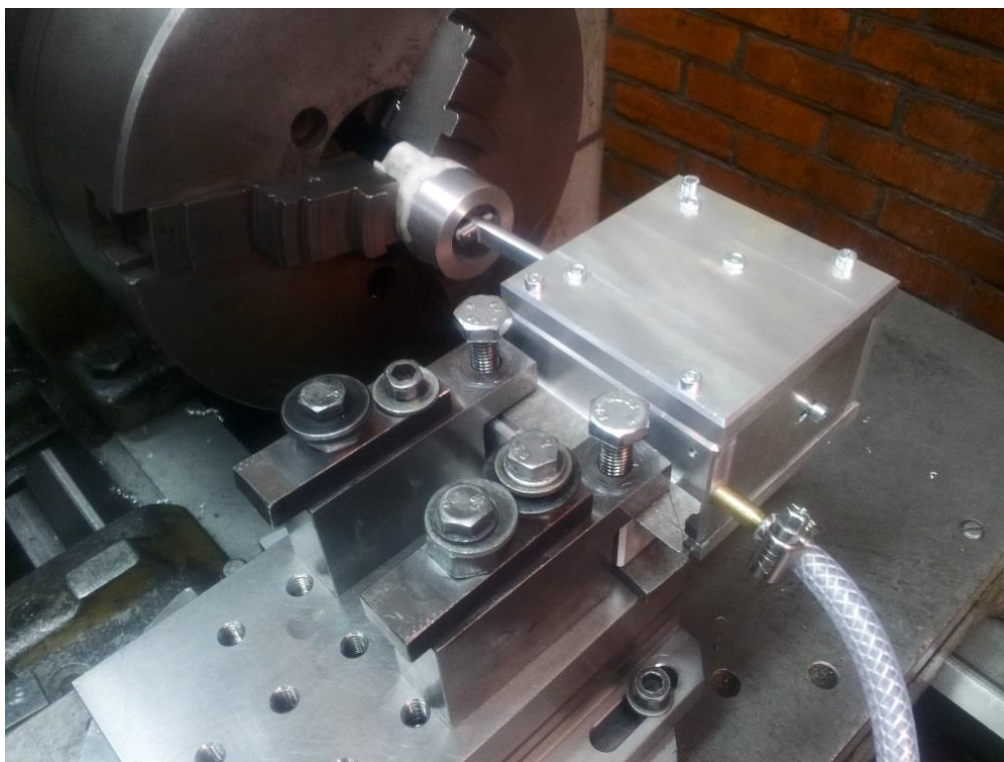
Установленная на станок пневматическая оправка на пружинах для внутреннего выглаживания
